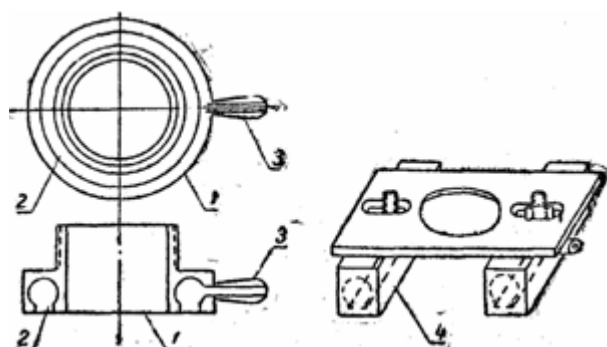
Приспособление для растягивания поверхности кожного покрова.
